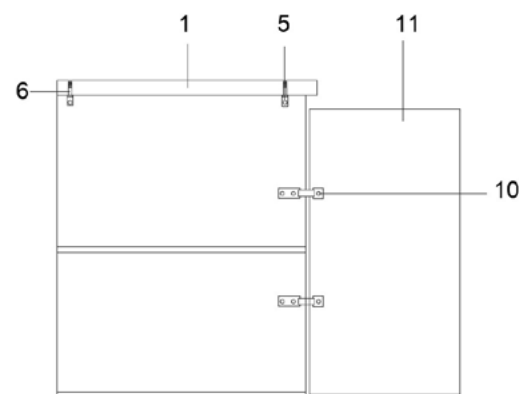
Detalle constructivo mueble de cocina con mesón de acero inoxidable
